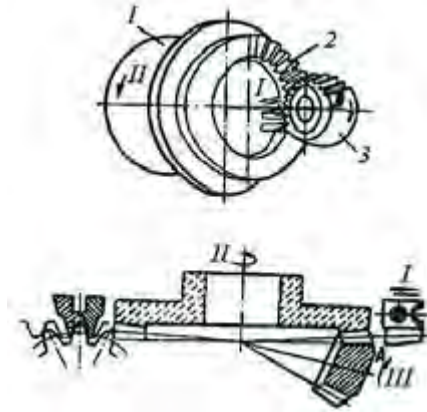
Схема нарізування зубців конічного прямозубого колеса на зубоштрівальному верстаті з конусним утворюючим колесом
